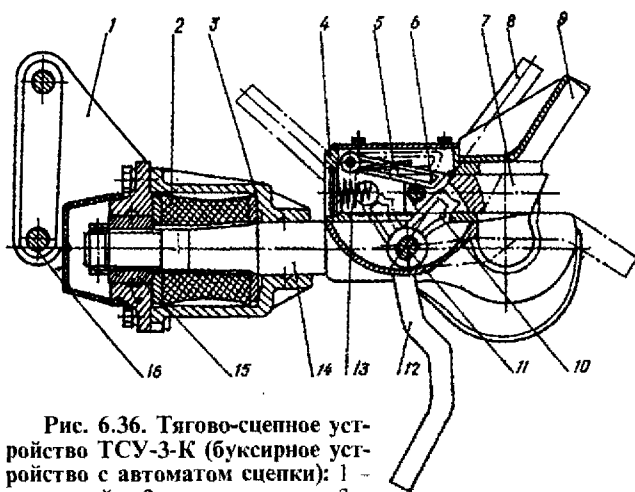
Тягово-сцепное устройство ТСУ-3-К (буксирное устройство с автоматом сцепки): 1 – кронштейн; 2 – амортизатор; 3 – колпак; 4 – корпус автомата сцепки; 5 – пружина; 6 – упор фиксатора; 7 – фиксатор зева; 8 – рукоятка управления фиксатором; 9 – козырек; 10 – рычаг фиксатора; 11 – ось рукоятки управления; 12 – нижний ловитель; 13 – пружина фиксатора; 14 – тяговый крюк; 15 – гайка крюка; 16 – палец
